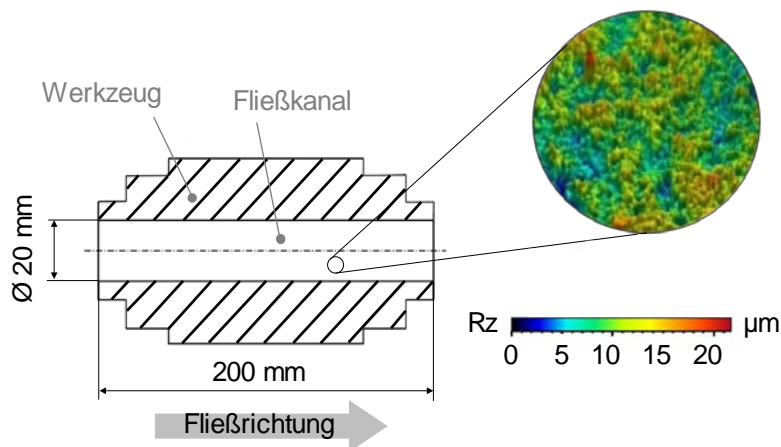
Schnittdarstellung des Extrusionswerkzeuges
